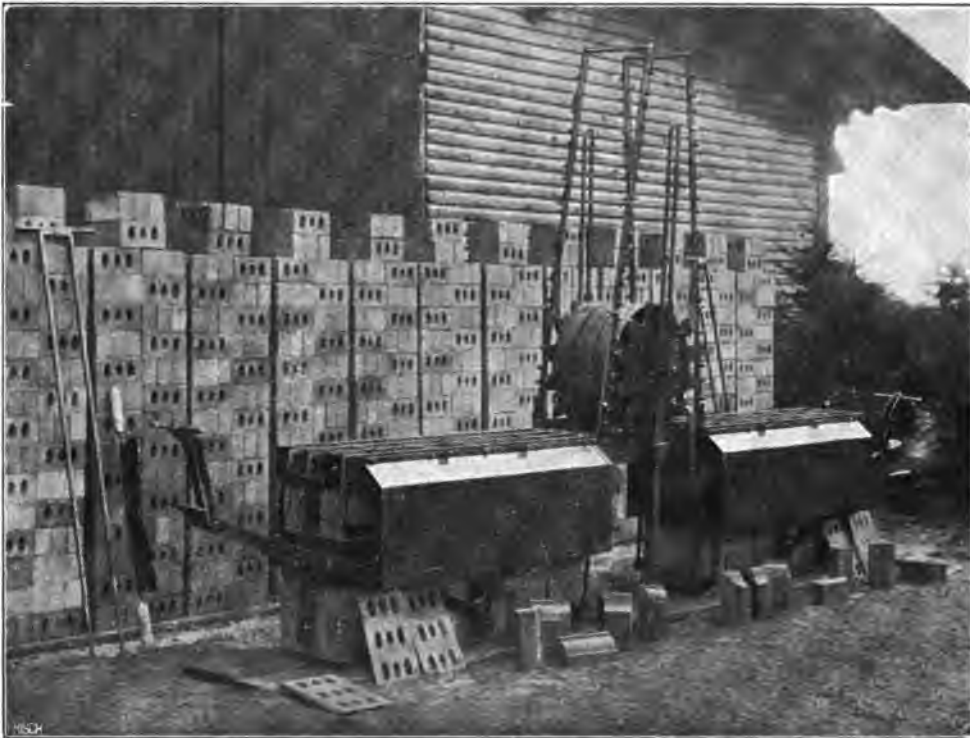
Zementmauersteinmaschine „Die Welt“ von J. P. Jörgensen.
